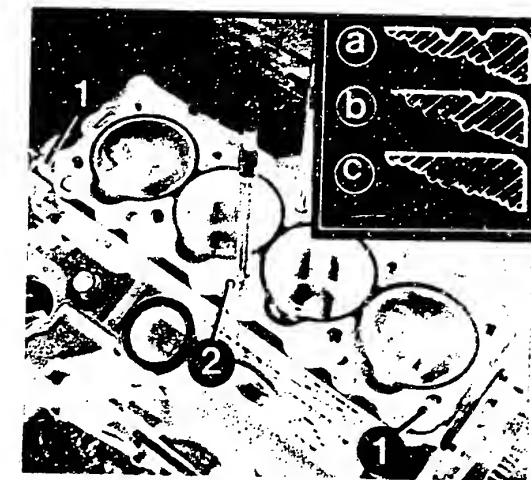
Dieselmotor: Um das Verdichtungsverhältnis in engen Toleranzen zu halten, gibt es drei verschieden dicke Zylinderkopfdichtungen: a) mit zwei Kerben, Dicke = 1,95 mm, bei Kolbenüberstand = über 0,75 mm – b) mit einer Kerbe, Dicke = 1,80 mm, bei Kolbenüberstand = 0,60 ... 0,75 mm – c) ohne Kerbe, Dicke = 1,65 mm, bei Kolbenüberstand = weniger als 0,60 mm. – 1 Zentrierstifte Zylinderkopf – 2 Ölkanal zur Nockenwelle.
